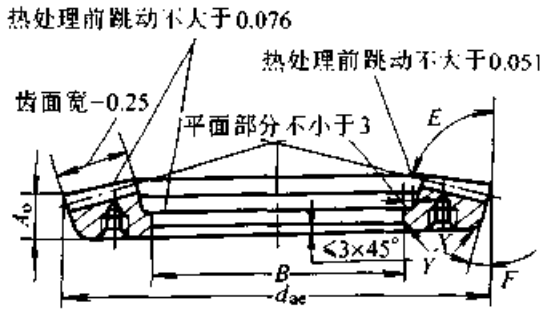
无凸缘环形齿轮的轮坯公差
